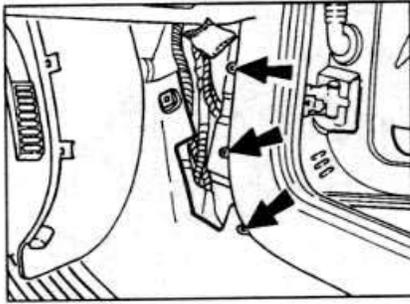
Расположение пружинных скоб крепления внутренней обивки.
